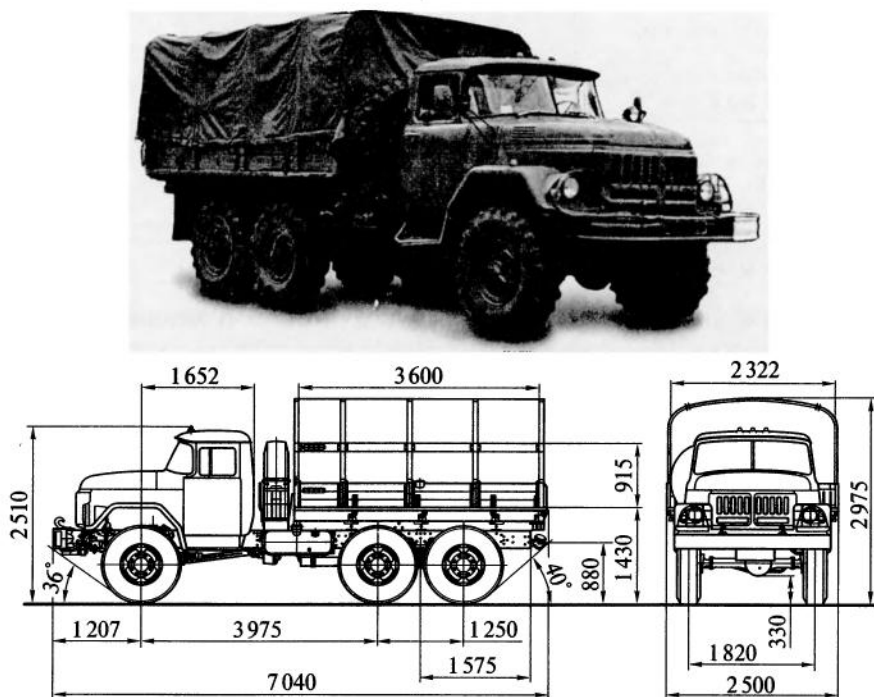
Бортовой автомобиль «Амур-5313»
